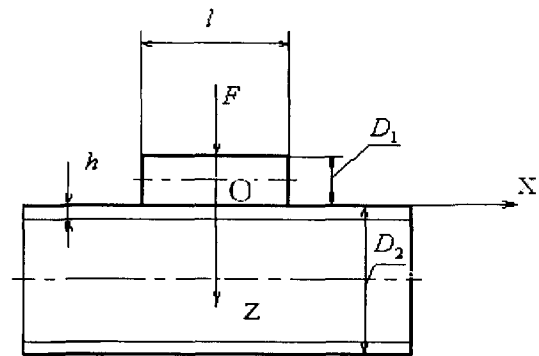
Схема деформирования роликом цилиндрической наплавленной поверхности
